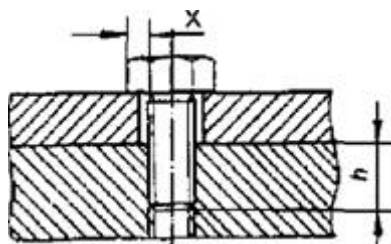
Допуски і зазор для різьбових з'єднань
